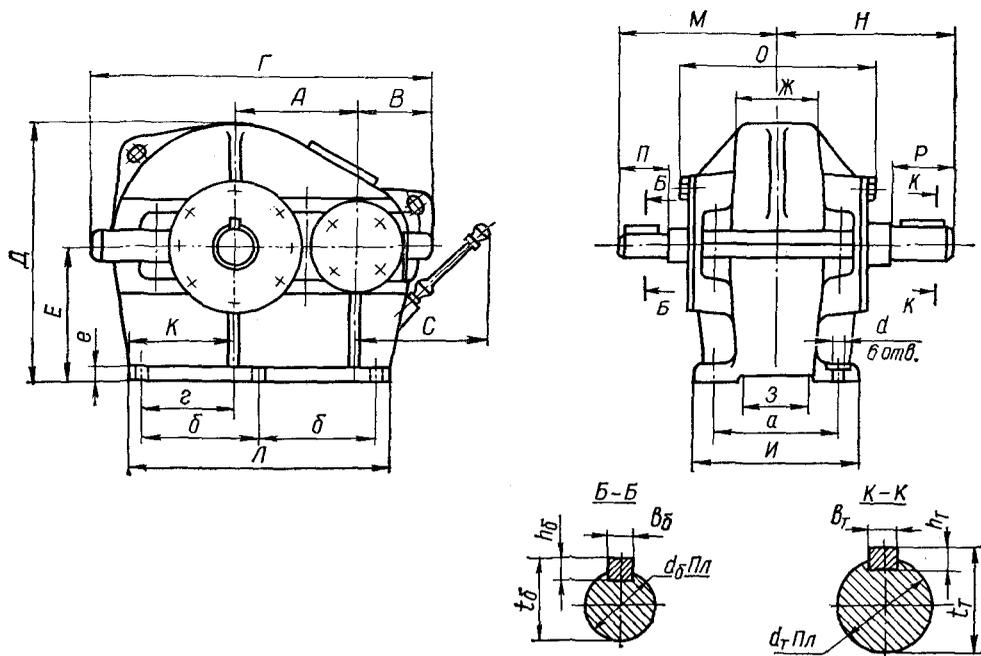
Основные и габаритные размеры редукторов ЦОН.
